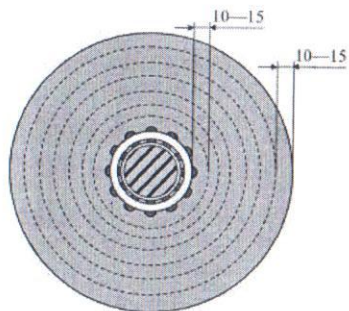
Круговой контроль венцов тормозных дисков
